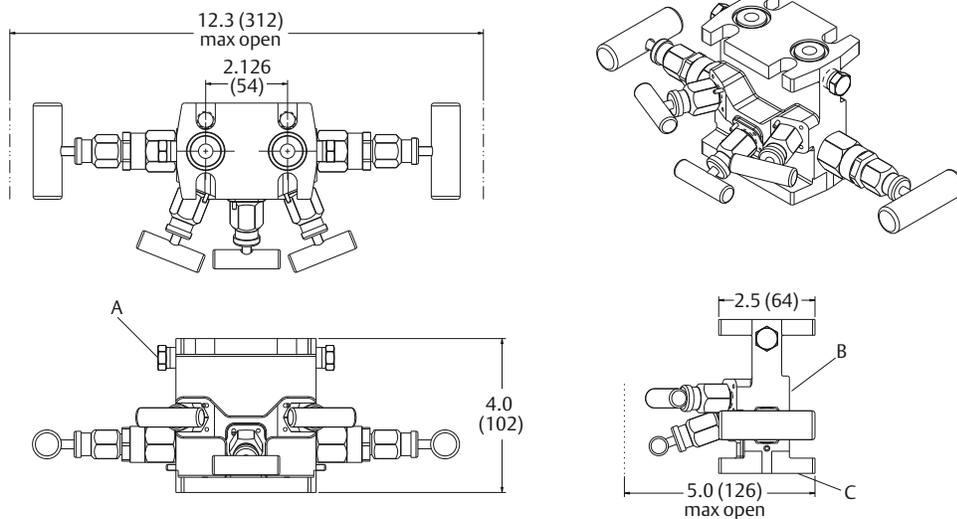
Традиционный клапанный блок 304 с пятью вентилями, конструкция фланец x резьба (гидравлическая схема для природного газа) с опцией NG
